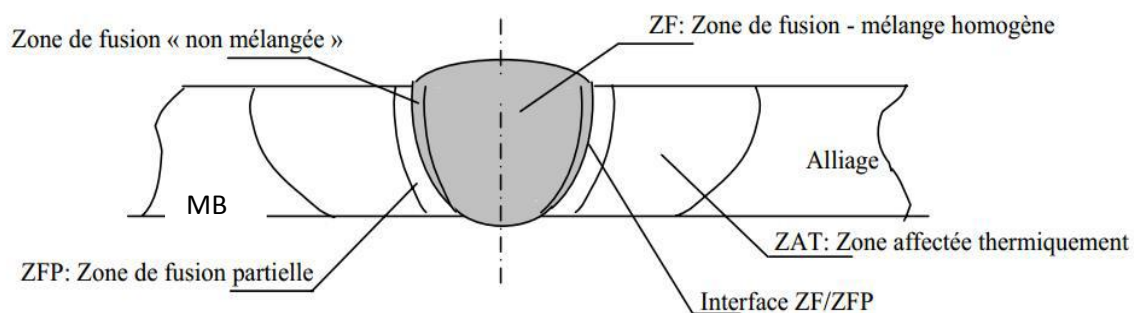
Présentation macrographique d'un joint soudé.
